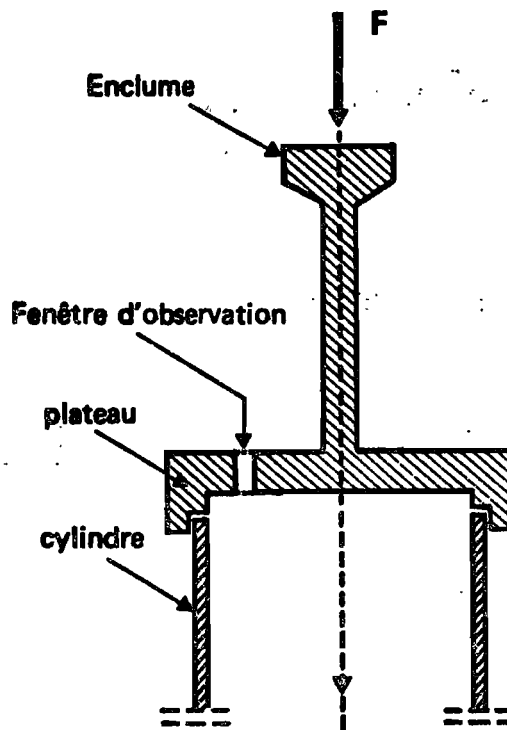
CASQUE-PLATEAU VU EN COUPE
